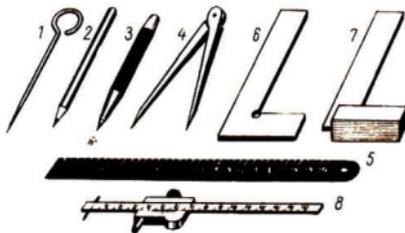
Anreißwerkzeuge für die Metallbearbeitung
